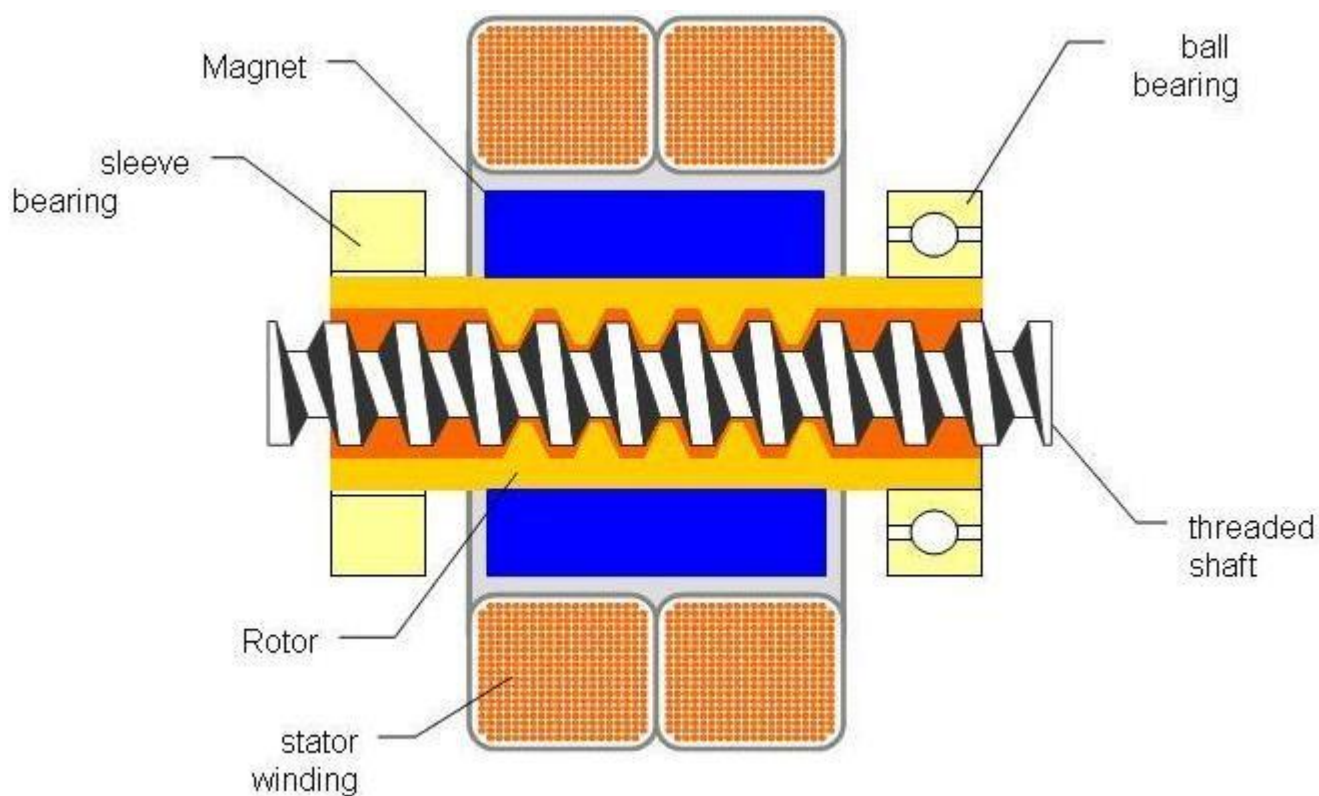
Actuador Idle Paso Sección Cross Motor
